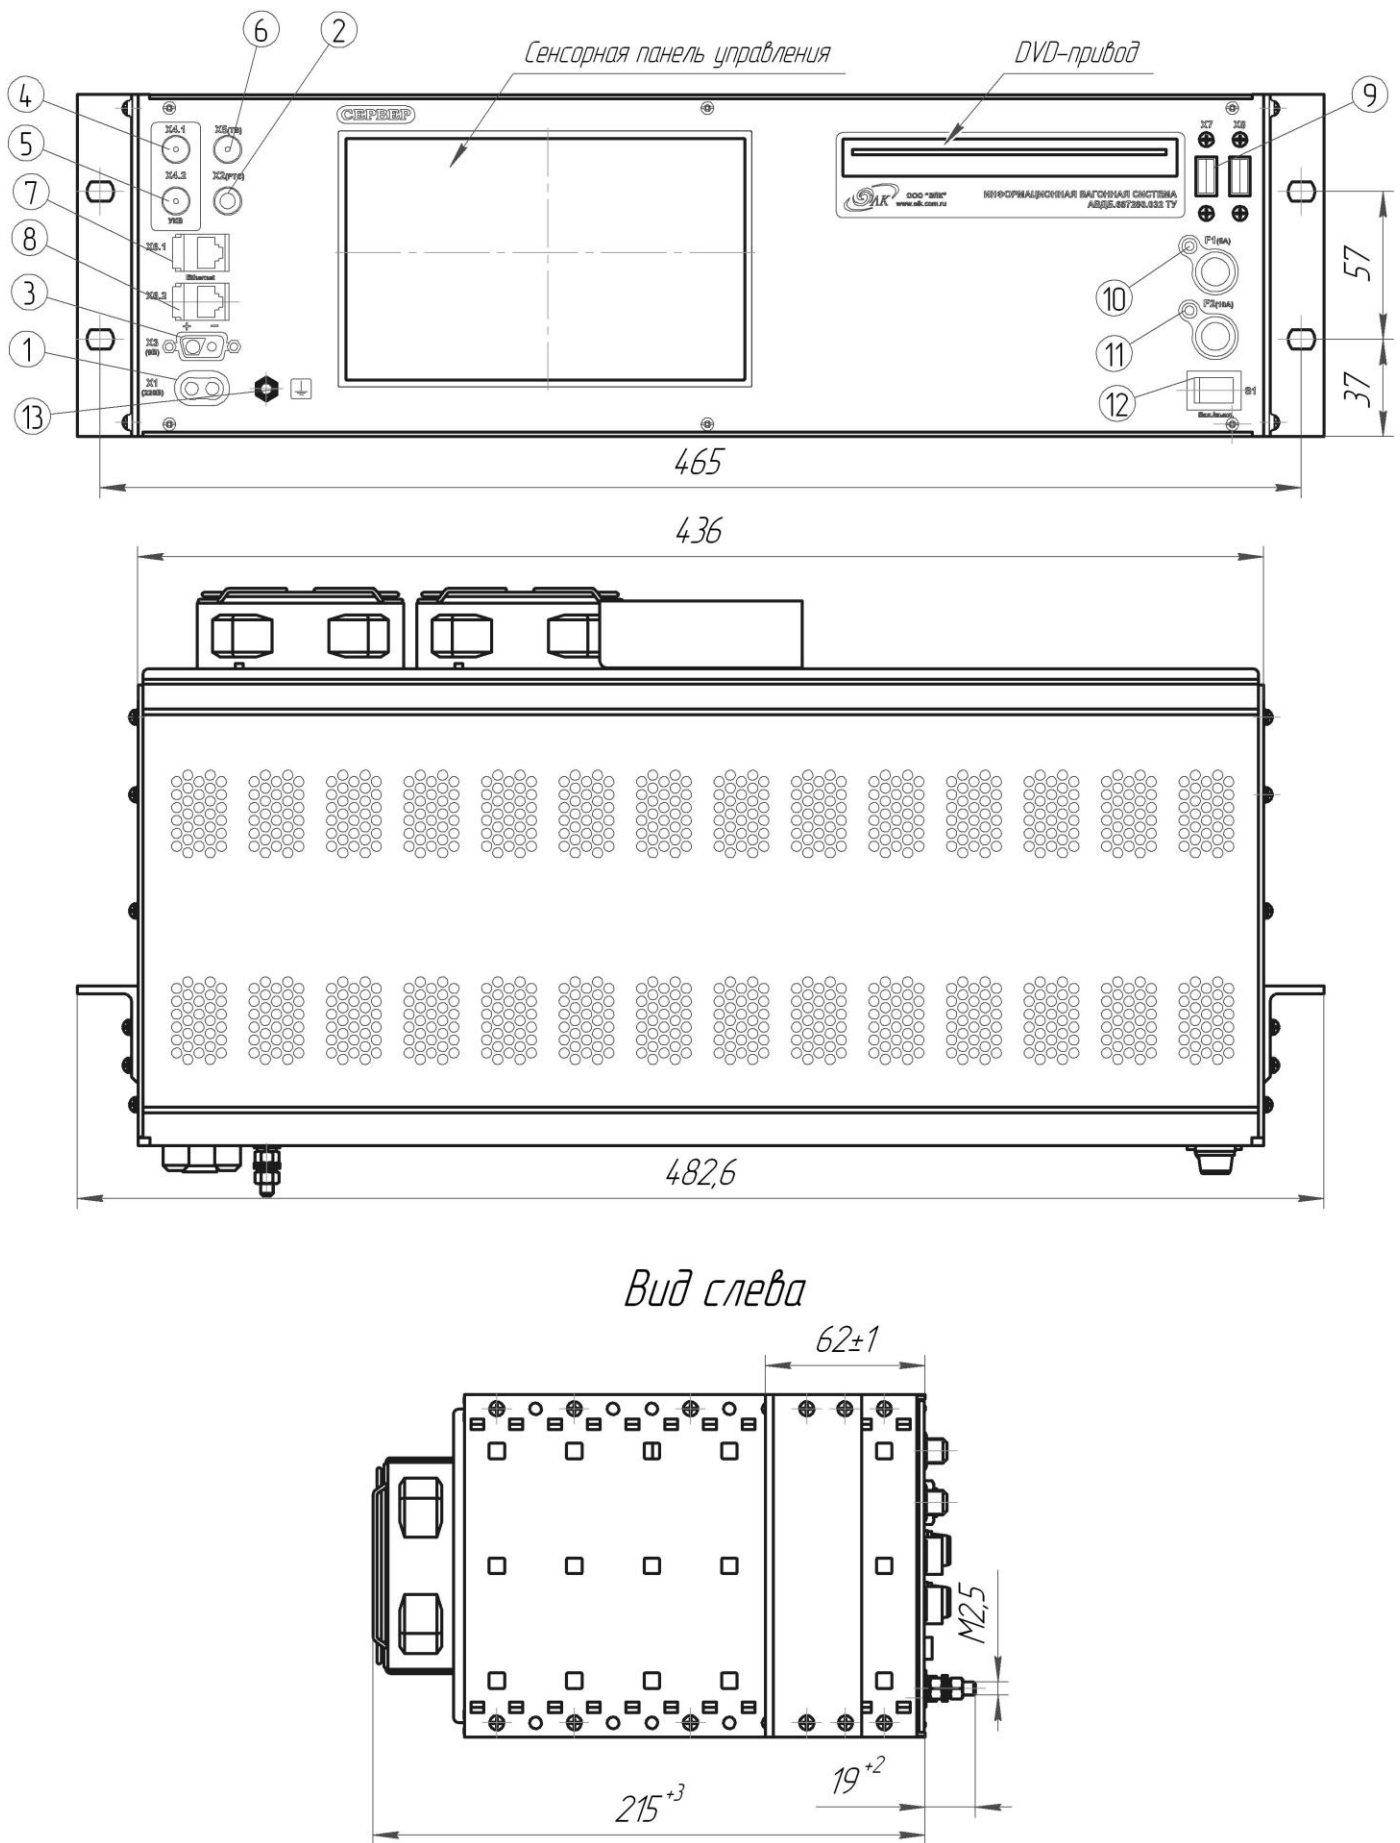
Внешний вид и габаритные размеры сервера-3.01.
